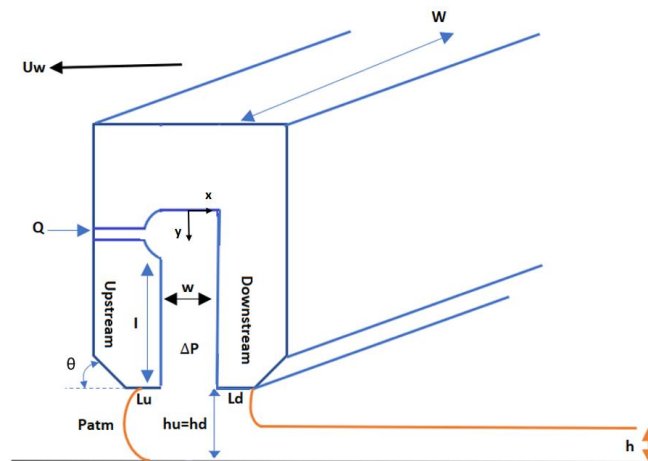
Dimensiones del cabezal. Fuente: Elaboración propia.
